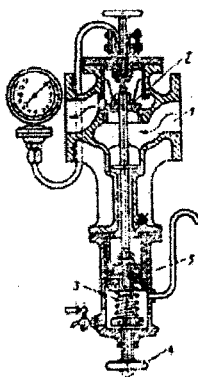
Редукційний клапан: 1 — канал; 2 — золотник;
